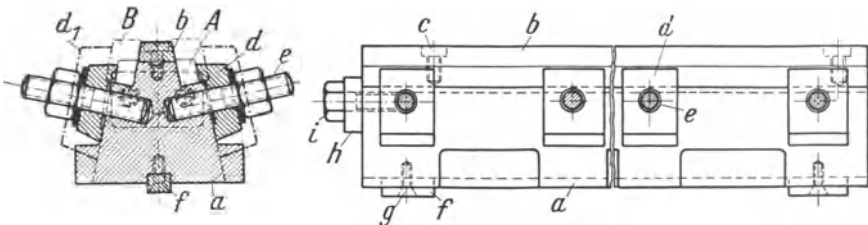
Fräsvorrichtung für Einsatzstücke zu Lünettenbacken.
